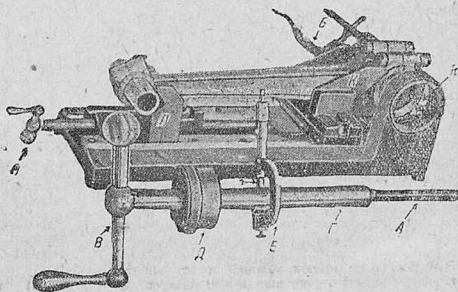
Установка шатуна в приспособлении для расточки подшипника
